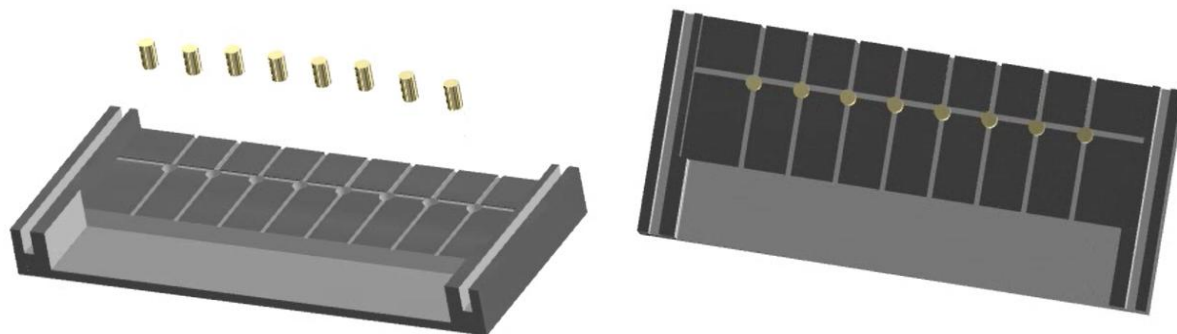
Suporte magnético fabricado com impressora 3D.
